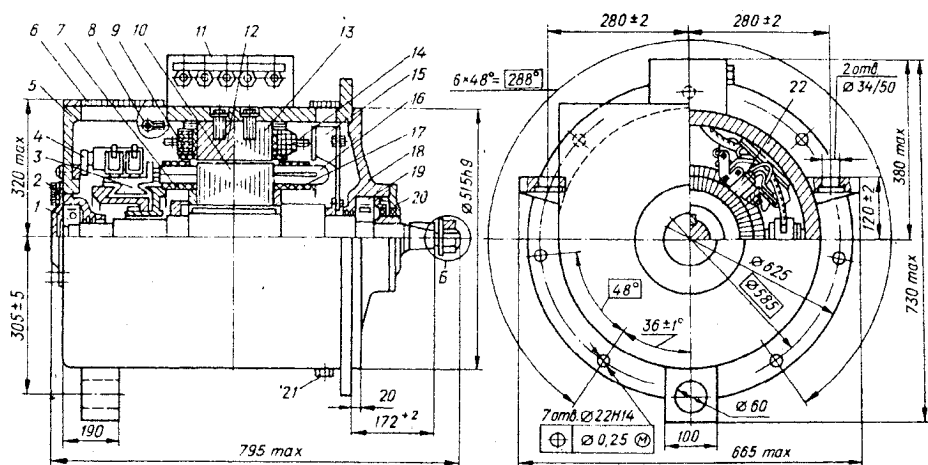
Конструкция тягового двигателя ДТН-45/27В
